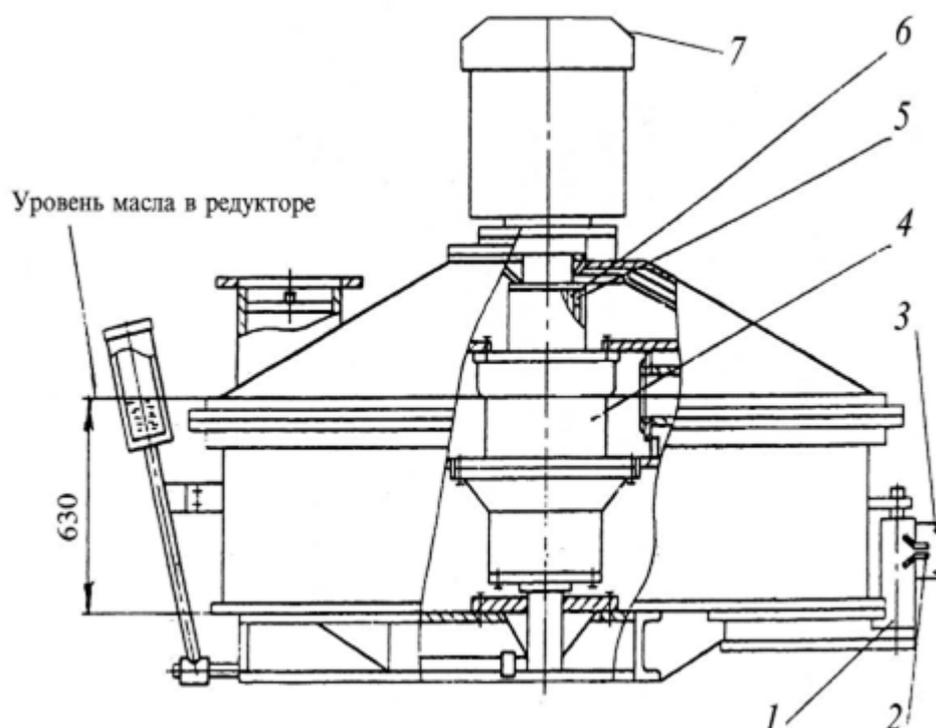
Схема смазки бетоносмесителя СБ-138Б: 1 – подшипник затвора; 2 – шарниры пневмоцилиндра; 3 – пневмоцилиндр; 4 – редуктор; 5 – верхний подшипник редуктора; 6 – лабиринтное уплотнение; 7 – электродвигатель.
